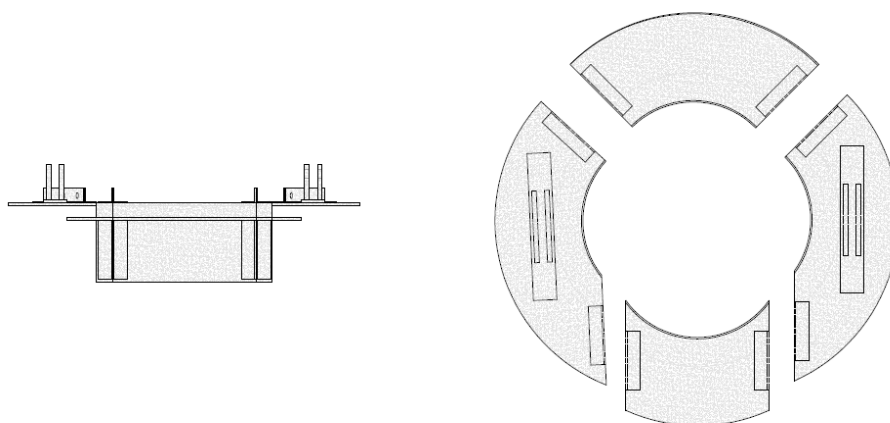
Vůle mezi spodním a horním dílem přesypu
